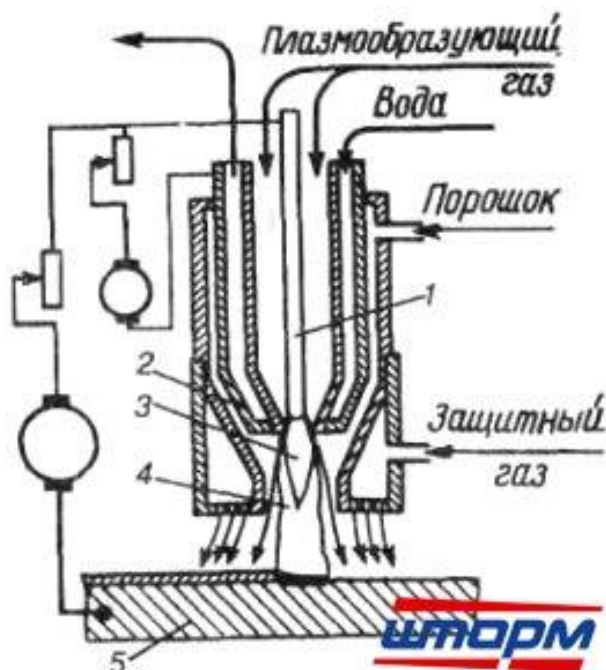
Схема плазменной наплавки с вдуванием порошка в дугу
